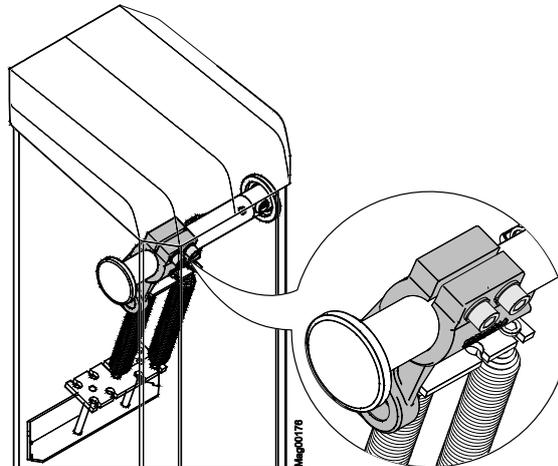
Innensechskantschrauben am Klemmhebel lösen
